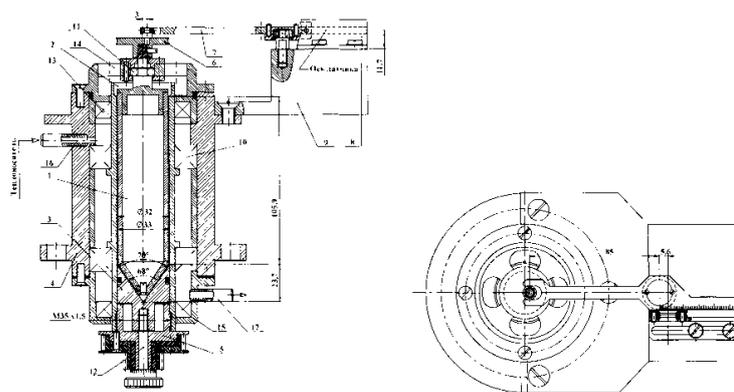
Измерительный блок ротационного вискозиметра: 1 – статор; 2 – ротор; 3 – подпятник; 4 – корпус; 5 – шкив синхронной передачи; 6 – кривошип; 7 – коромысло; 8 – датчик момента; 9 – кронштейн; 10 – подшипник ротора; 11 – подшипник статора; 12 – винт регулировки конического зазора; 13 – манжета пружинная; 14, 15 – верхняя и нижняя крышки; 16, 17 – штуцеры ввода и вывода теплоносителя
